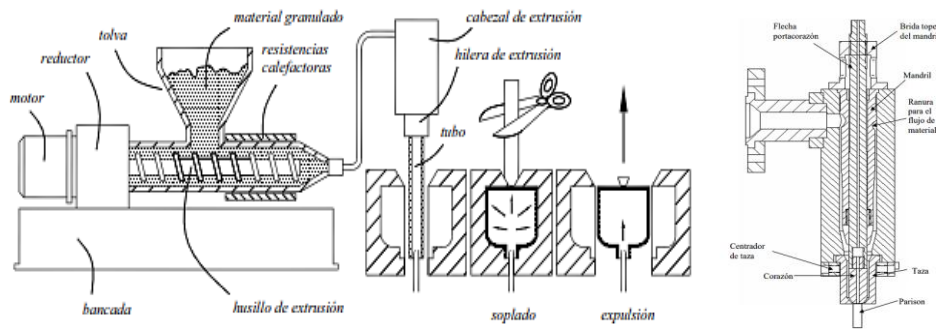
Elementos de la máquina de soplado a) (derecha) máquina de soplado b) (izquierda) cabezal de extrusión
